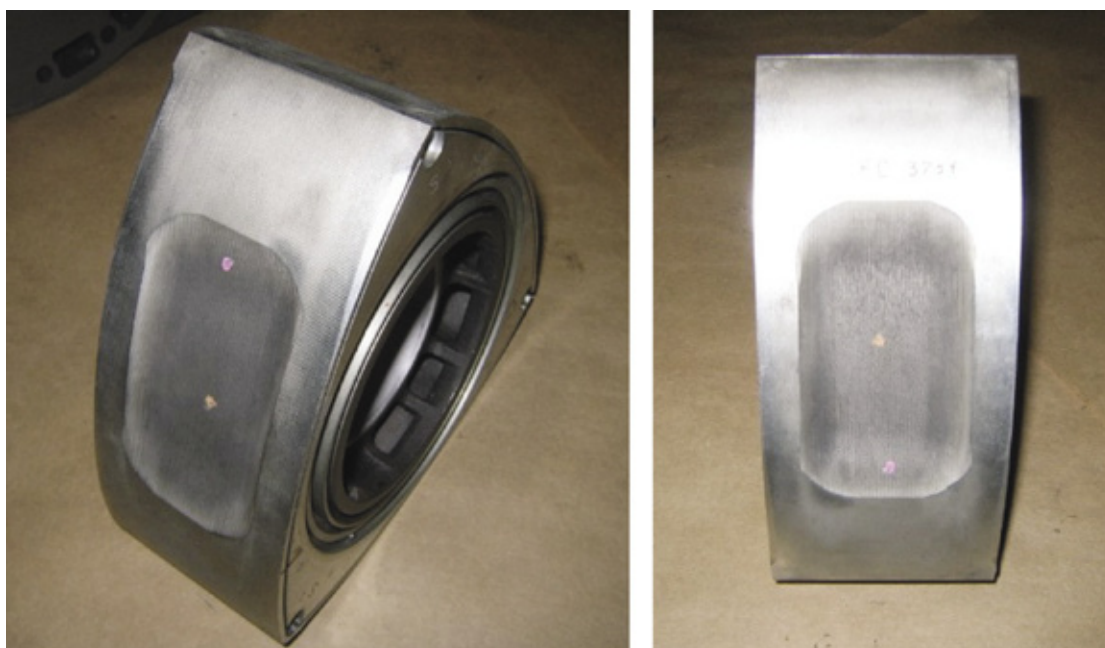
Внешний вид ротора РПД. Двигатель ВАЗ-311
